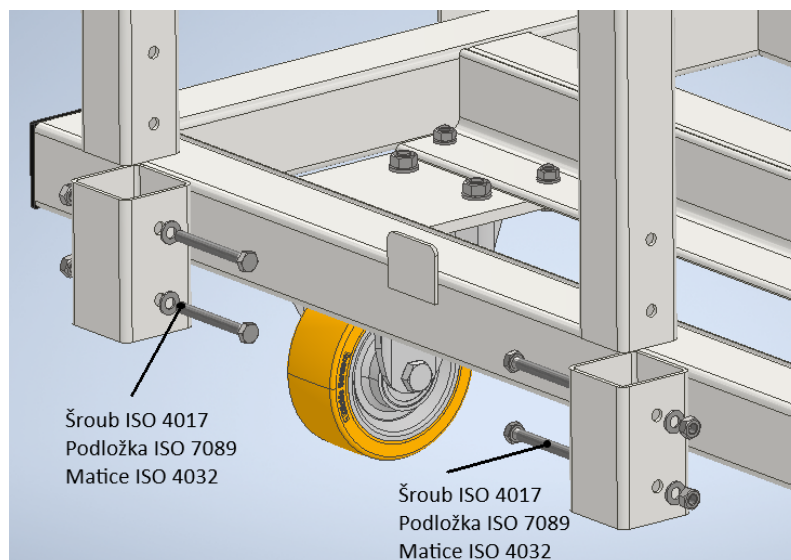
Spojení rámu s výměnnou deskou a konzolou kola pomocí šroubových spojů
